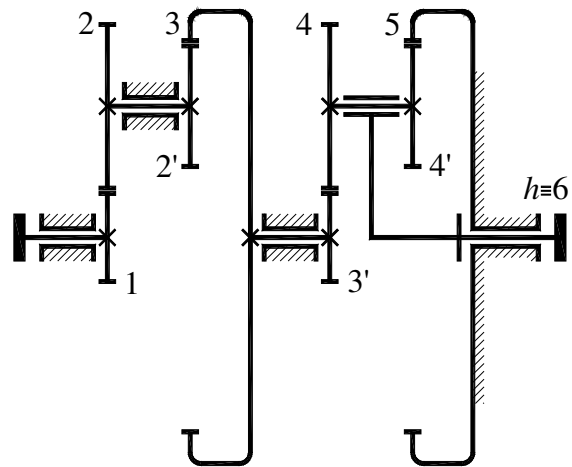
Планетарный механизм Давида с двумя внешними зацеплениями
